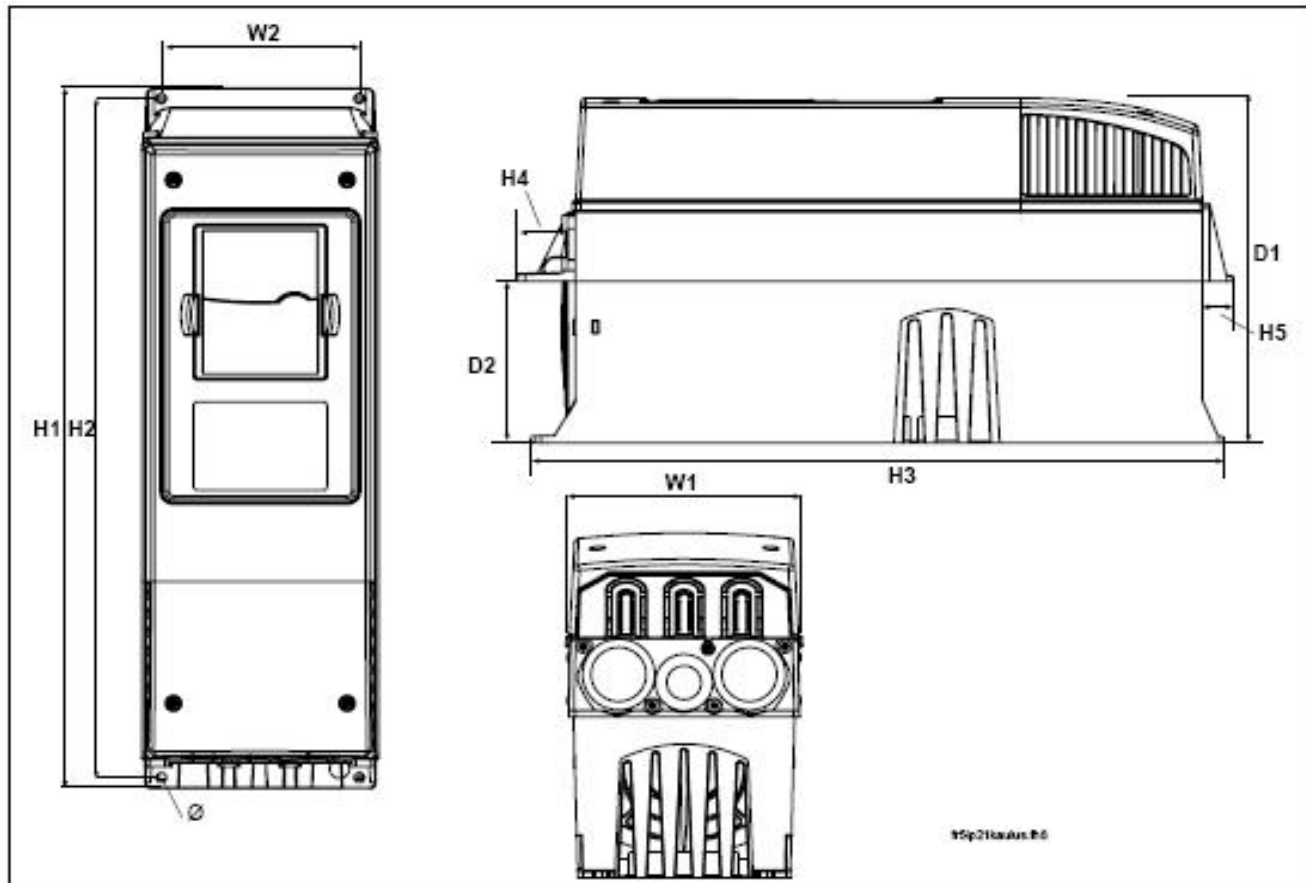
Dimensões Vacon NX, FR4 a FR6; Montagem por flange
